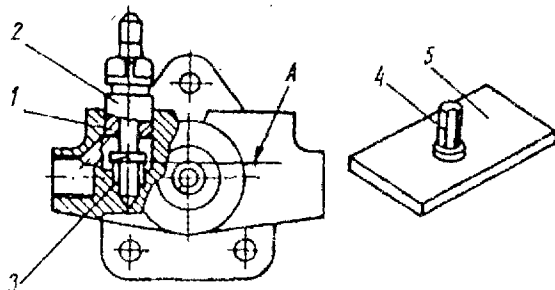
Приспособления для ремонта топливоподкачивающего насоса: 1 - зенкер; 2 - втулка; 3 - гнездо клапана; 4 - клапан; 5 - плита
